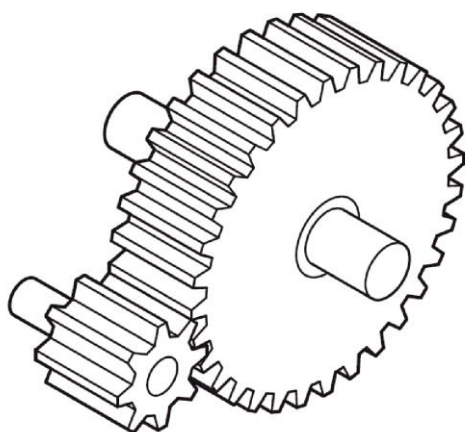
Прямозубая цилиндрическая зубчатая передача.
